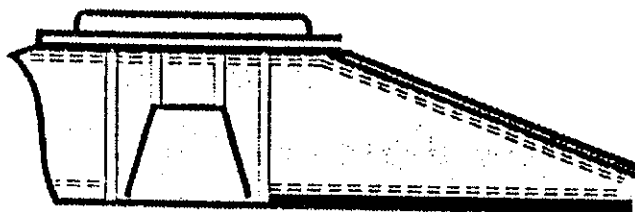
Контроль сварного соединения боковой стенки с верхней и нижней пластинами
